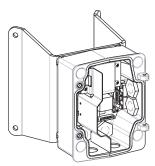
Boîtiers d'alimentation en montage mural, sur mât et en angle
